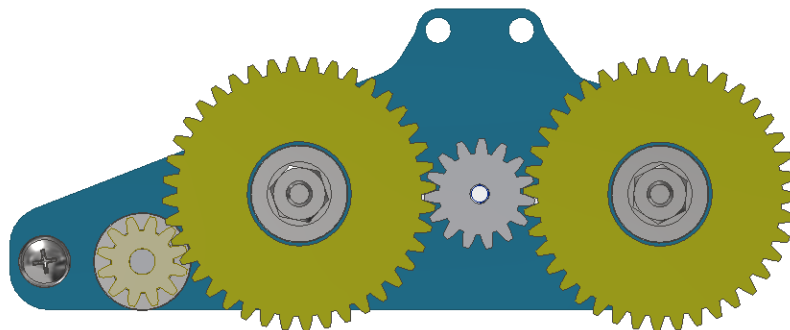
, Vista frontal, engranaje-rueda-motor
